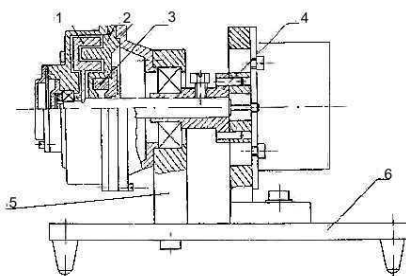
Стенд для испытания редуктора и нагрузочного устройства. 1 - ротор демпфера; 2 - корпус демпфера; 3 – магнитное уплотнение, состоящее из постоянного магнита, магнито проводящего контура и магнитной жидкости в зазоре между корпусом и ротором; 4 - муфта, для стыковки с выходным валом редуктора; 5 -стойка; 6 -плита.
